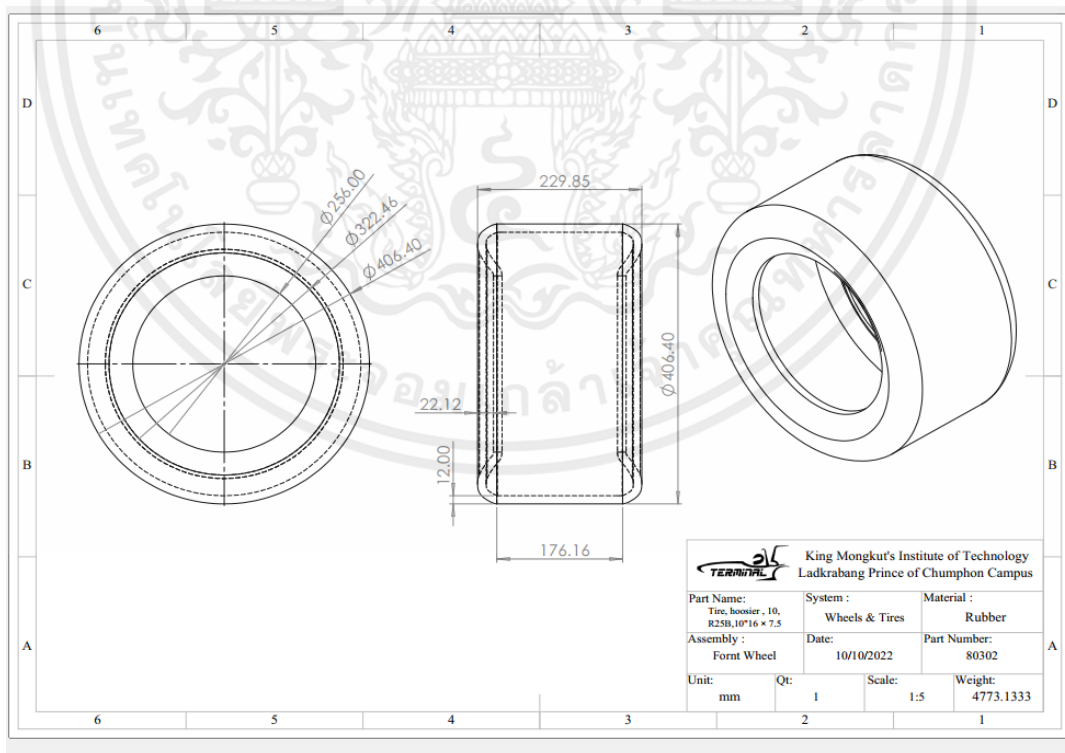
ส่วนประกอบของล้อ (wheel Assembly)
